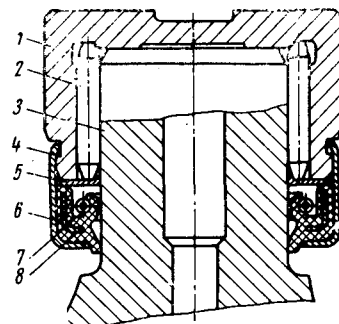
Уплотняющее устройство шарнира карданного вала автомобиля ЗИЛ:
